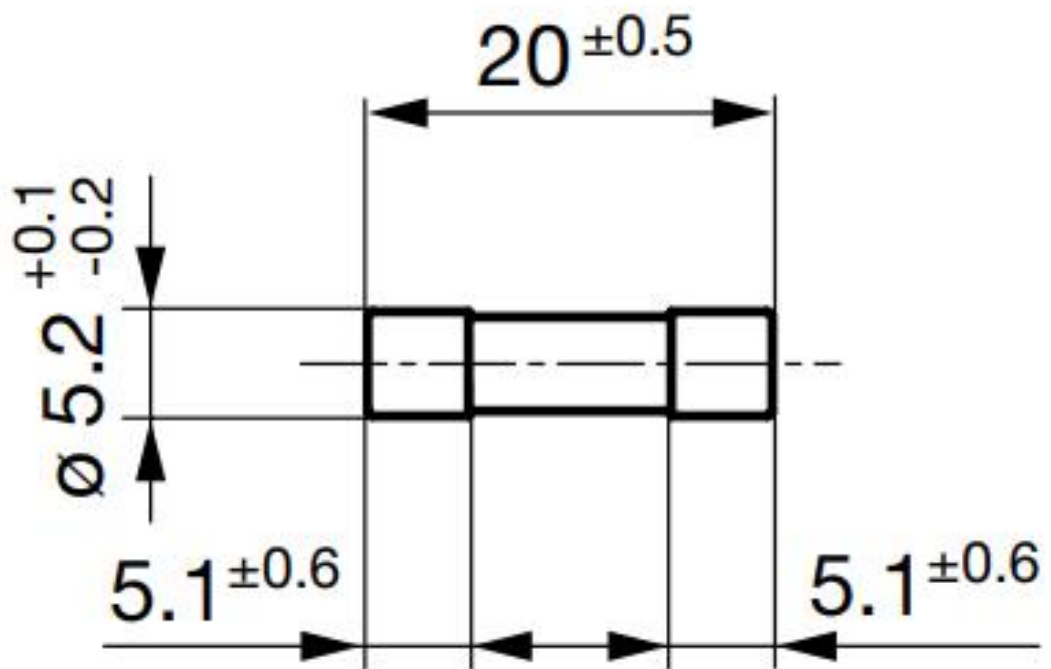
Габаритні розміри запобіжника серії FSF
